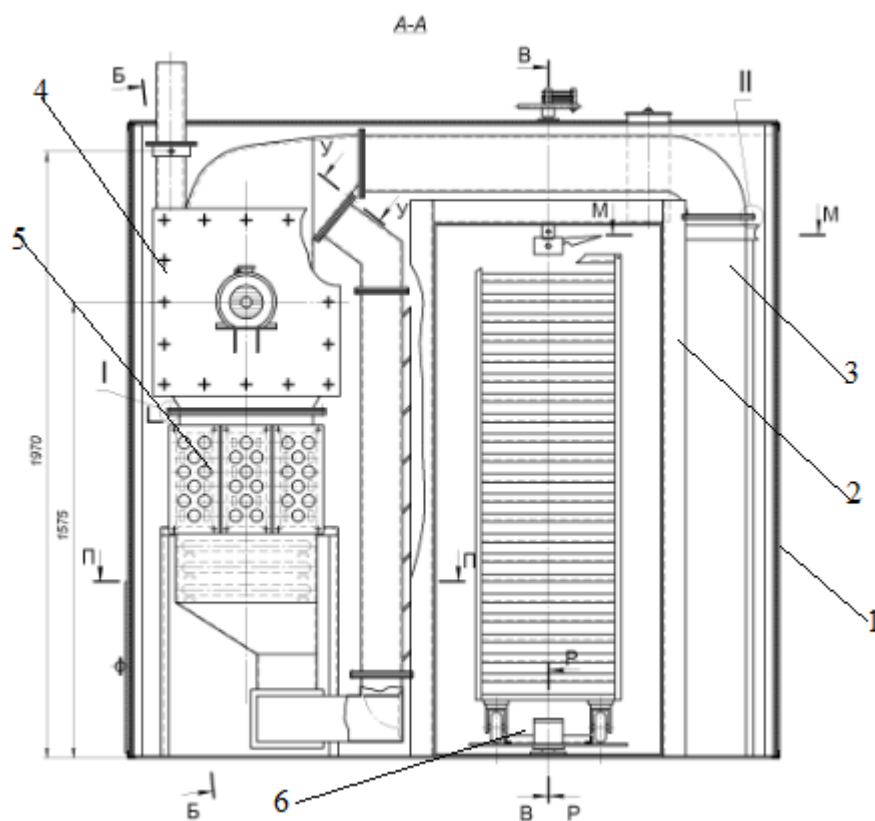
Розріз печі КЕП-400: 1 – металевий каркас; 2 – пекарна камера; 3 – короб подачі повітря; 4 – вентелятор; 5 – фільтр; 6 – механізм обертання вагонетки
